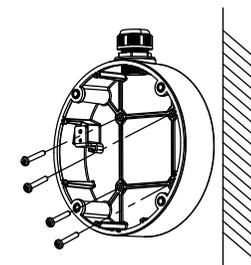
Befestigung des Gehäuses des Anschlusskastens an der Decke/Wand
